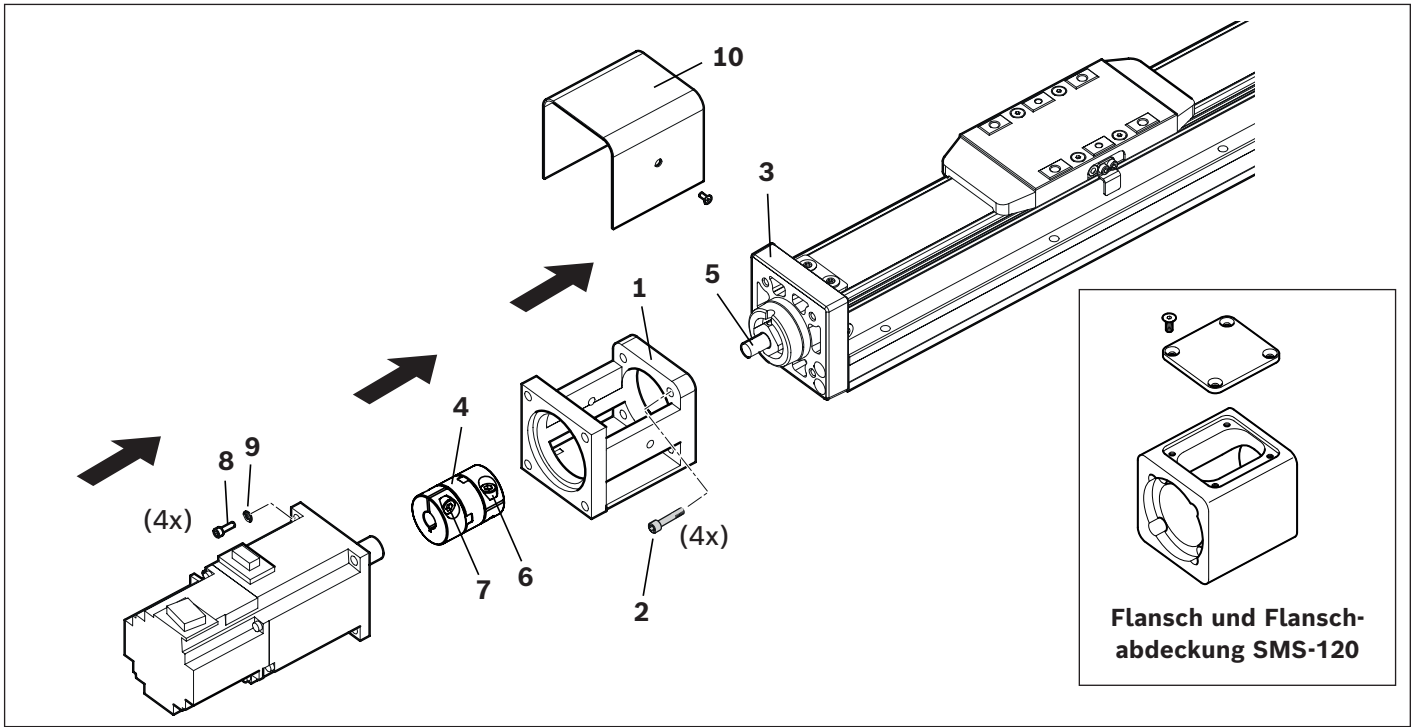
Motor mit Flansch und Kupplung montieren (SMS-040 – SMS-120)
